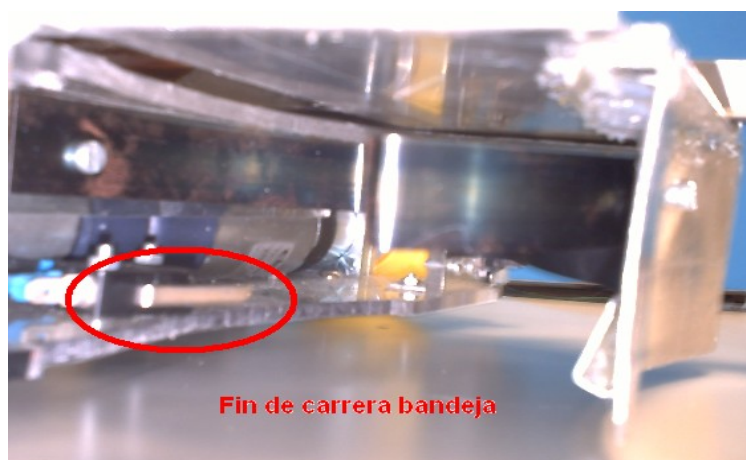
Detalle de sensor fin de carrera de la bandeja.
